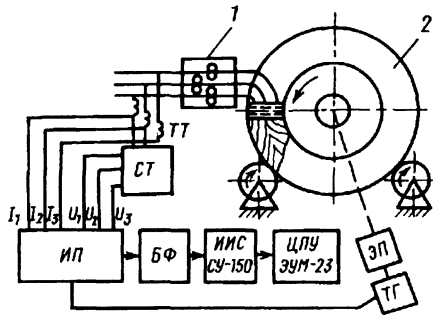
Схема подключения ИИССУ-150 к установке для ЭШС кольцевых швов: 1 — сварочный аппарат; 2 — изделие; БФ — блок фильтров; ЭП — электродвигатель (остальные обозначения см. рис. 3.8)
